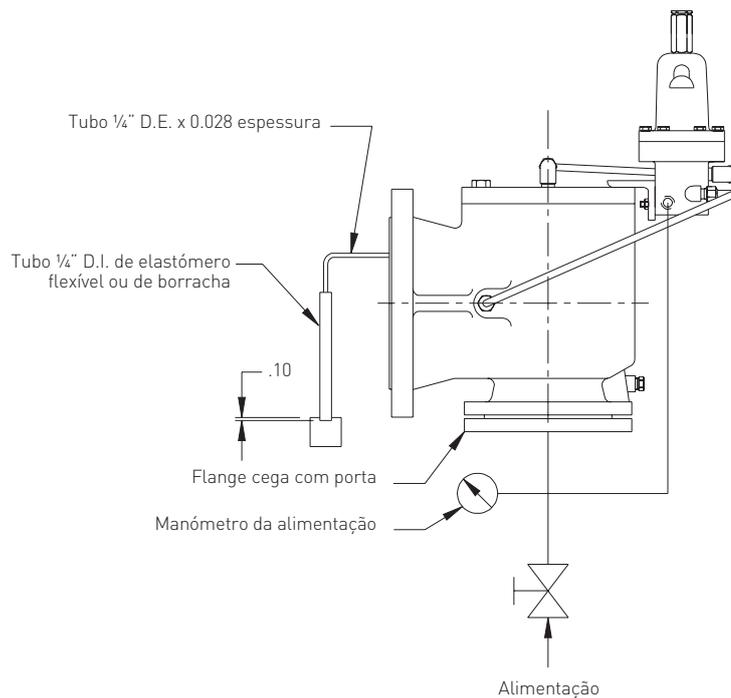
DISPOSITIVO DE ENSAIO PARA VÁLVULAS COM PILOTO DE DETECÇÃO REMOTA
